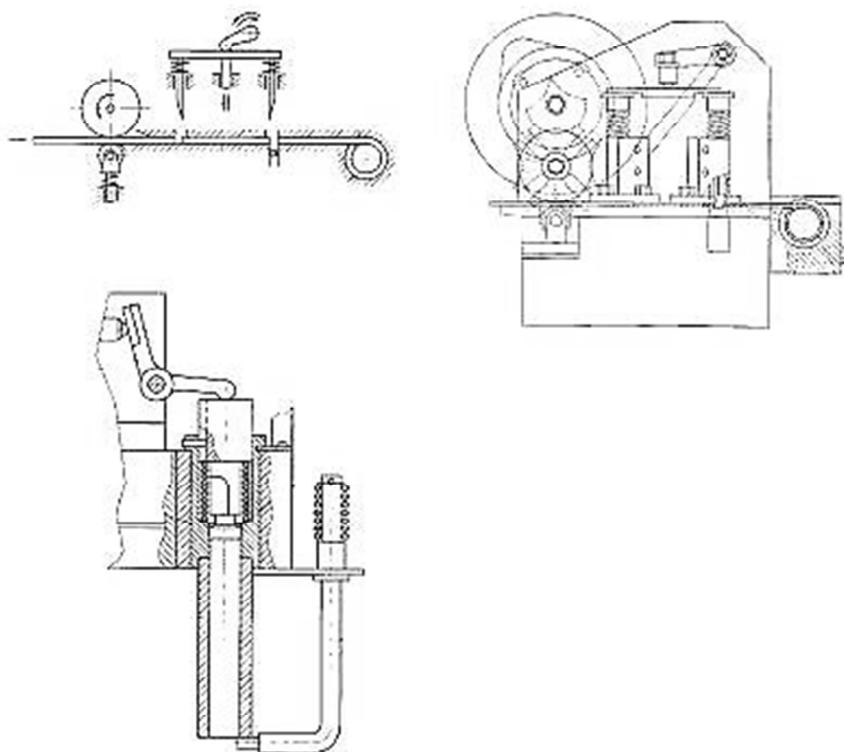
Автоматизированный способ [3] изготовления разрезных колец из полимерного материала
